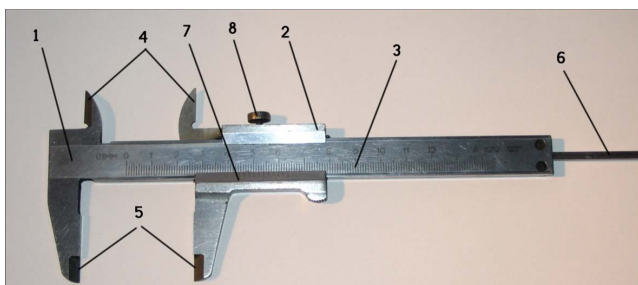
Устройство штангенциркуля: 1 – штанга; 2 – подвижная рамка; 3 – шкала штанги; 4 – губки для внутренних измерений; 5 – губки для наружных измерений; 6 – глубиномер; 7 – нониус; 8 – зажимный винт для фиксации рамки
